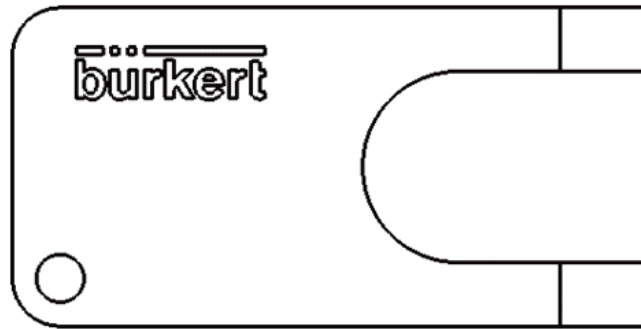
Werkzeug zum Ausbauen des Faltenbalgs
